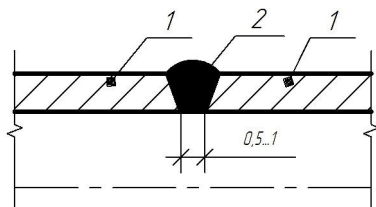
Зварювання пластмасових труб нагрітим газом: 1- з'єднувальні кінцівки труб, 2- зварний шов.
